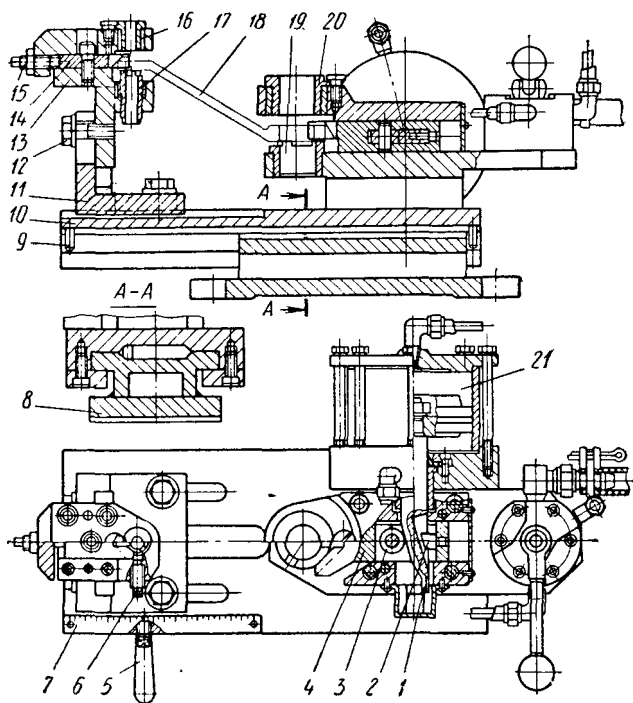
Универсально-наладочное приспособление для групповой обработки изогнутых рычагов
